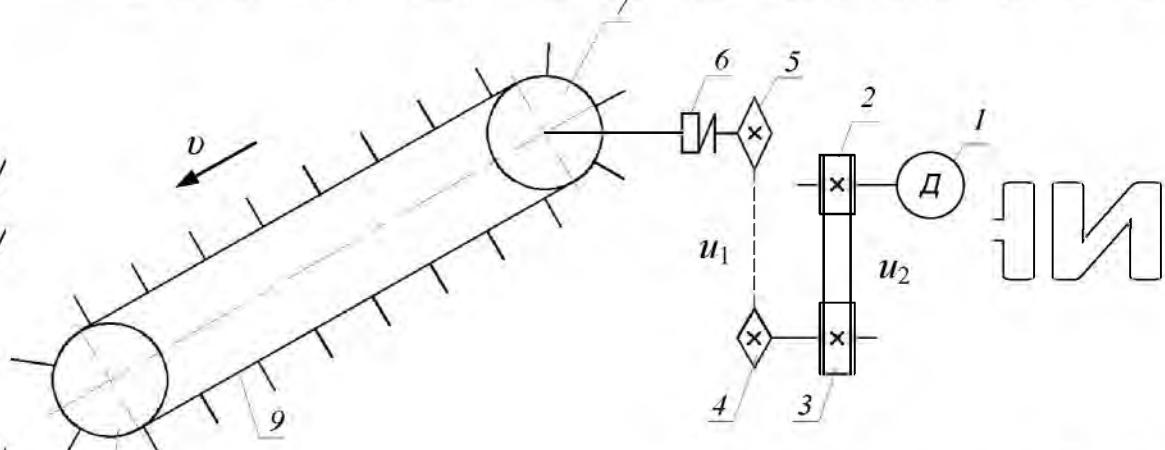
Кінематична схема скребкового конвеєра: 1 – двигун; 2, 3 – шківи пасової передачі; 4, 5 – зірочки ланцюгової передачі; 6 – муфта; 7 – приводна зірочка; 8 – приводна зірочка скребкового конвеєра; 9 – ланцюг зі скребками
